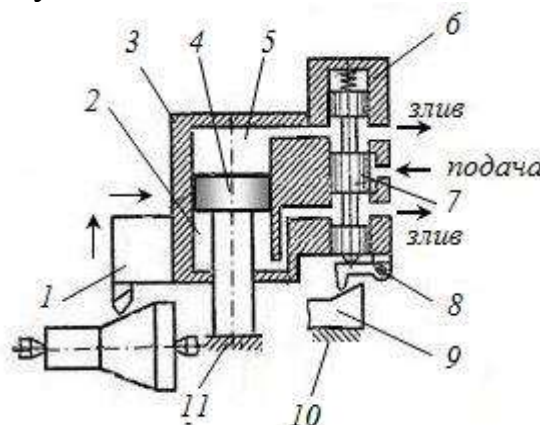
Схема слідкуючого гідроприводу поперечної подачі супорта копіювального токарного верстата: 1 – супорт верстата; 2,5 – порожнини робочого гідроциліндра; 3 – корпус гідроциліндра; 6 – гідророзподільвач; 7 – золотник; 8 – шуп; 9 – копір; 10 – корпус верстата; 11 – корпус супорта
